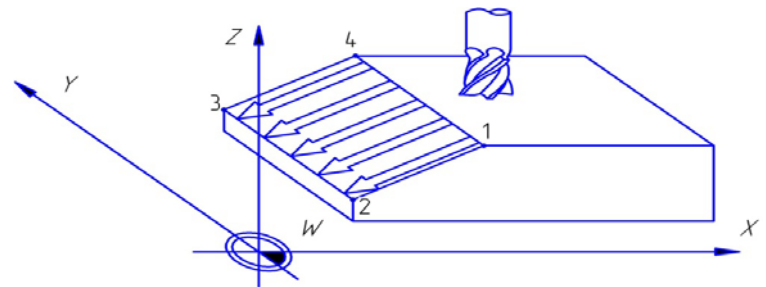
Фрезерование поверхности заготовки, наклонной к оси X
